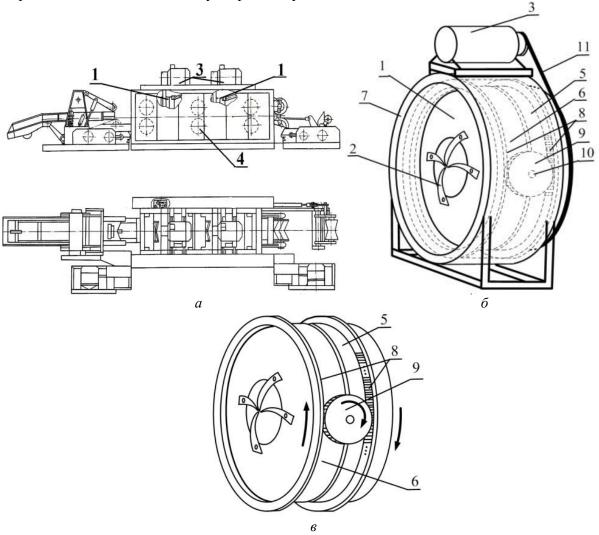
Конструкция двухроторного окорочного станка: a — двухроторный станок марки «2ОК63-1»; δ — общий вид; ϵ — принцип действия
